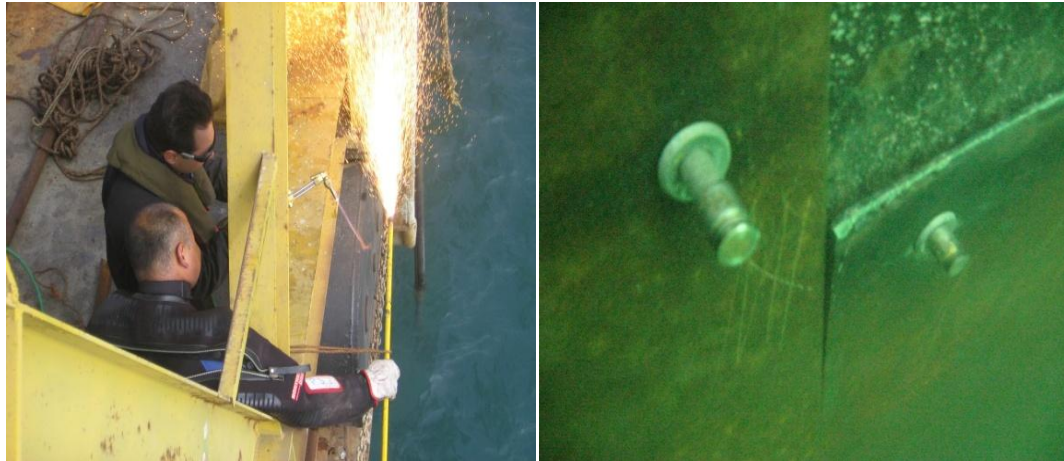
y N°6 Acciones de obturación mediante soldadura.
